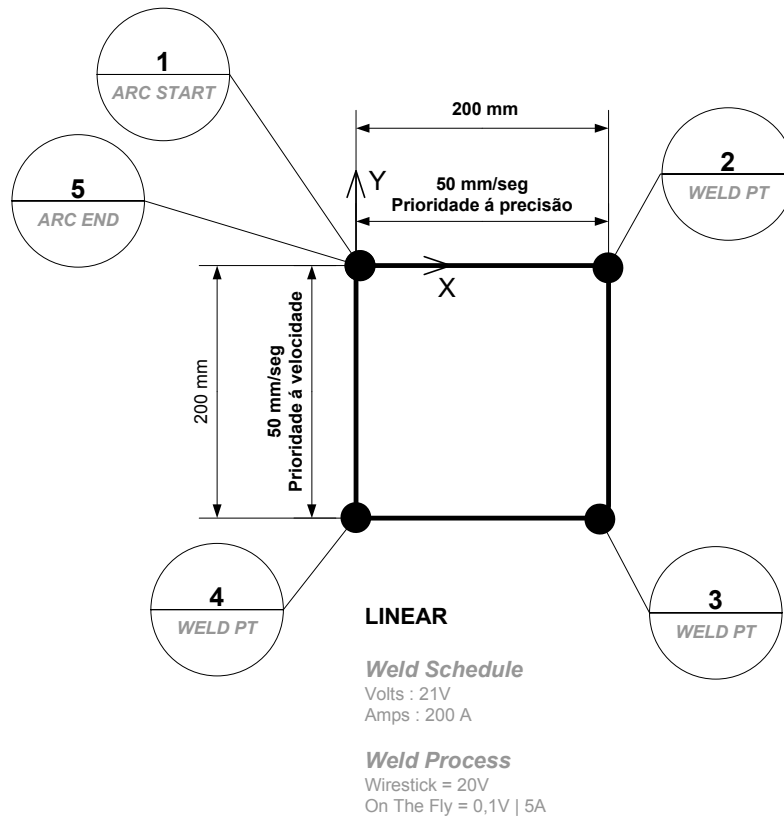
| Exercício 2 – Cordão de soldadura sobre um quadrado
